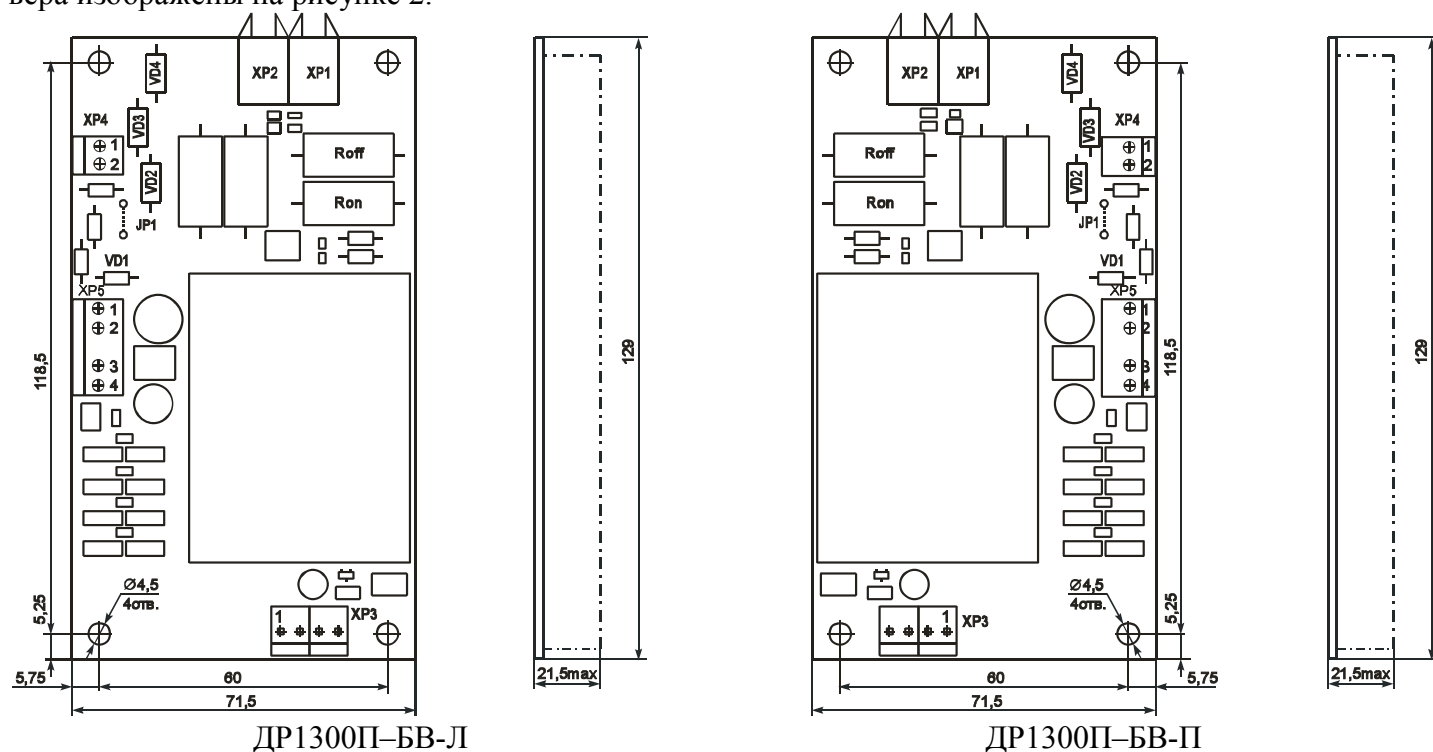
Габаритные и присоединительные размеры драйверов
